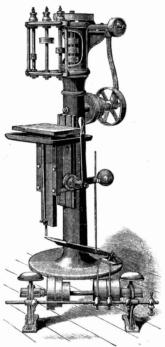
Gefühlsbohrmachine der Pratt & Whitney Co. Hartford. 1876.
